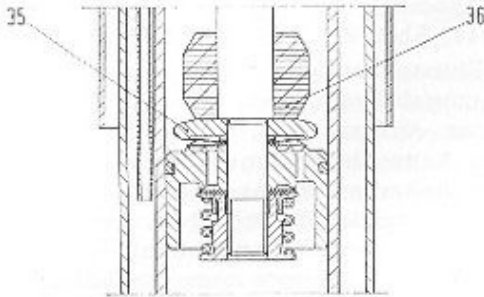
Teilquerschnitt durch einen hinteren hydr. Stossdämpfer.
